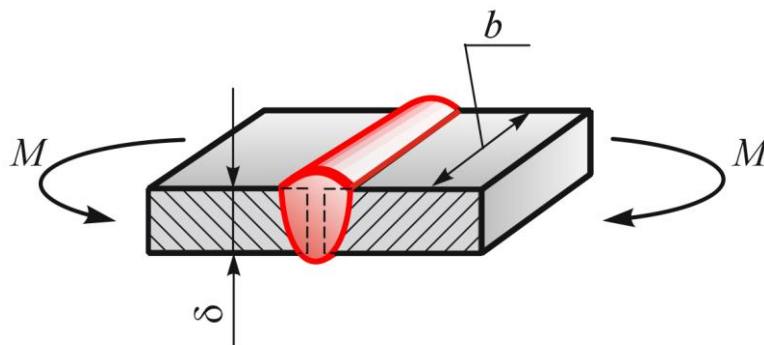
Схема нагружения сварного стыкового соединения изгибающим моментом
